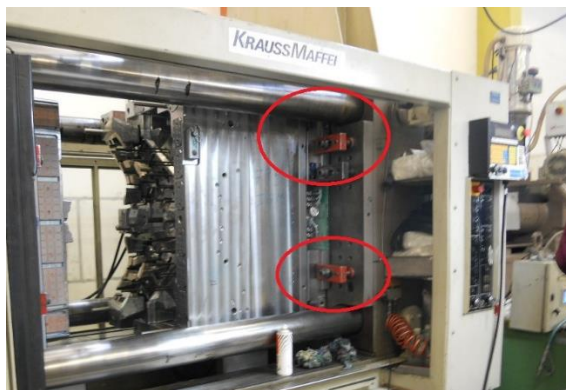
Cuidado de molde fixa na máquina de injeção (Simoldes Plásticos, 2018)
